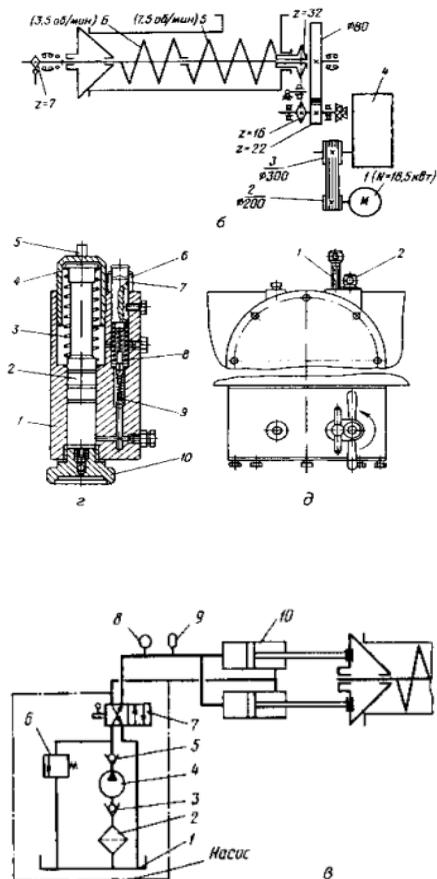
Пресс ВПО-30А: б – кинематическая схема(1,2 –
